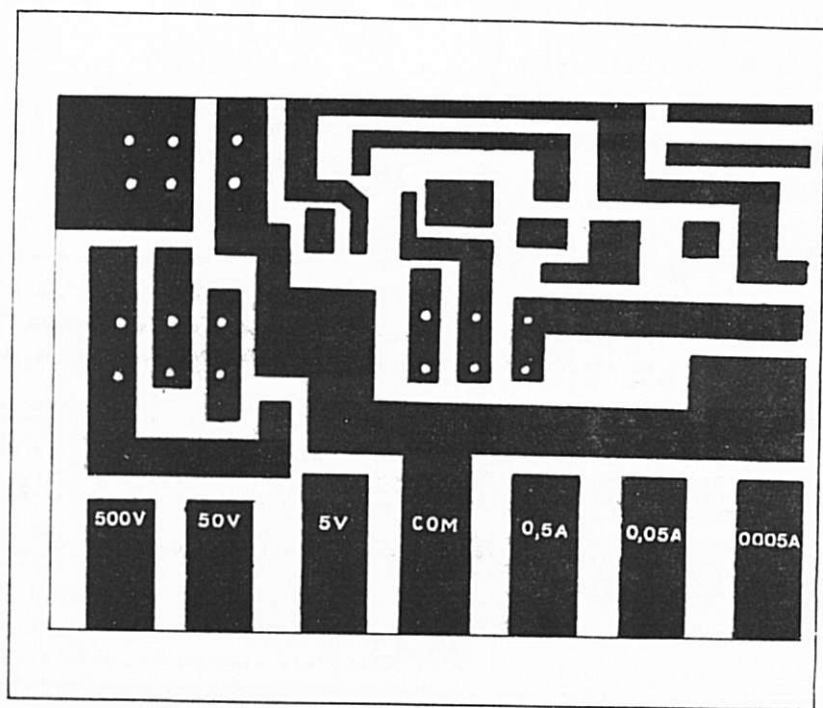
Desenho de parte do circuito impresso do multímetro. Os pon-
